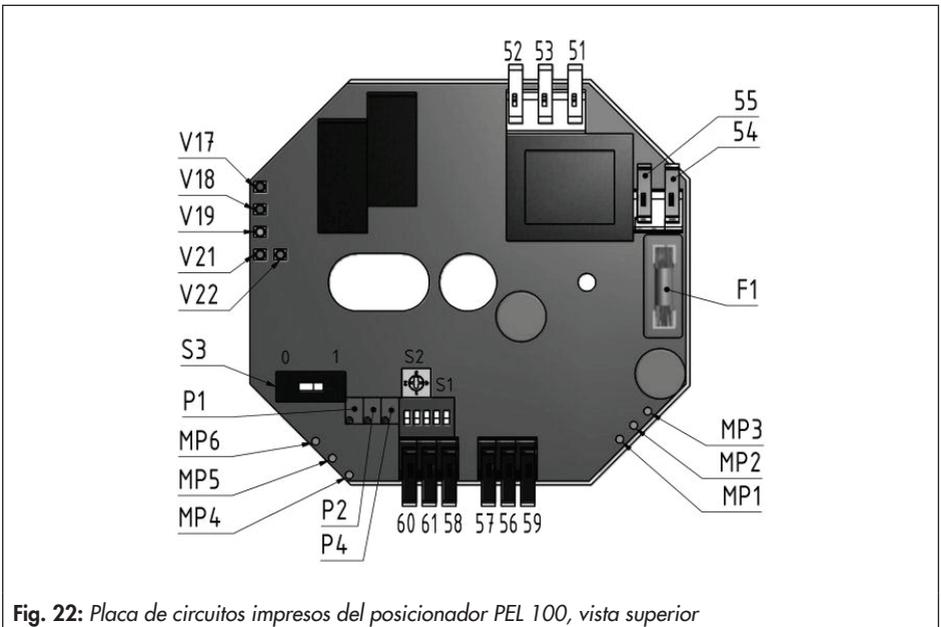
Placa de circuitos impresos del posicionador PEL 100, vista superior
